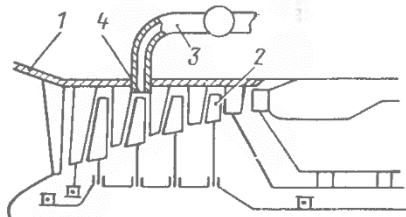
Схема усовершенствованного заборника воздуха от компрессора реактивного двигателя. Познции те же, что на рис. 4.13.
